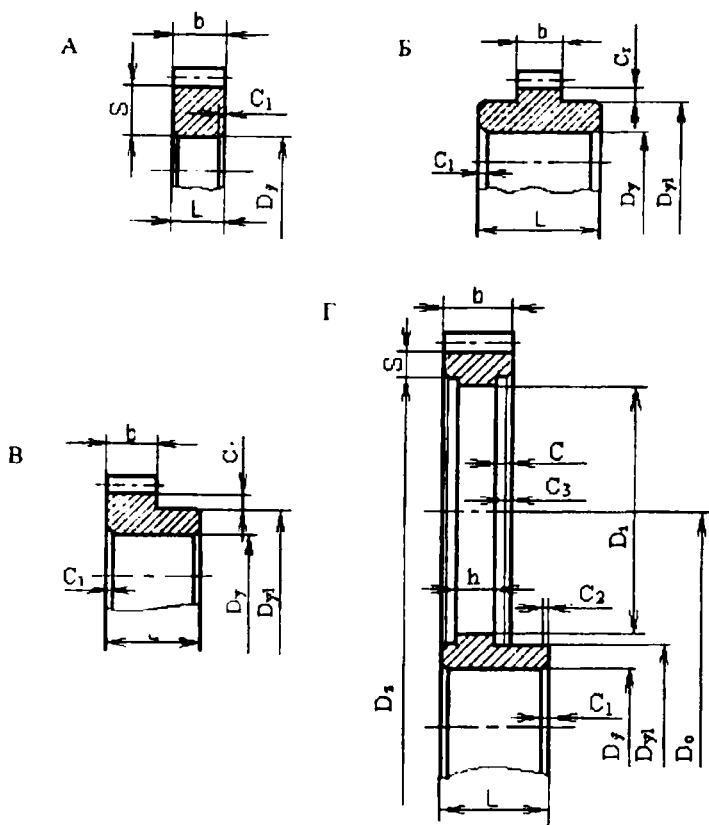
Примеры конструктивного оформления зубчатых колес
